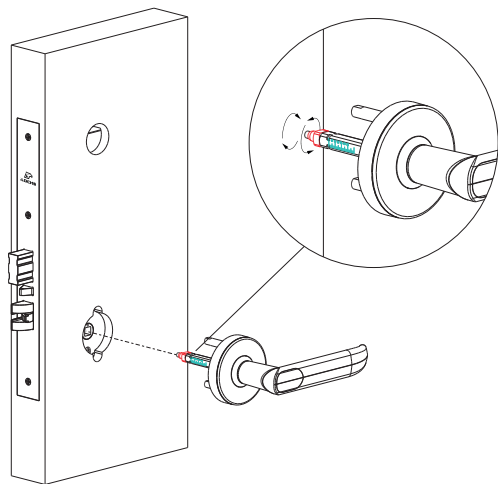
Регулировка квадрата и установка передней (внешней) ручки
